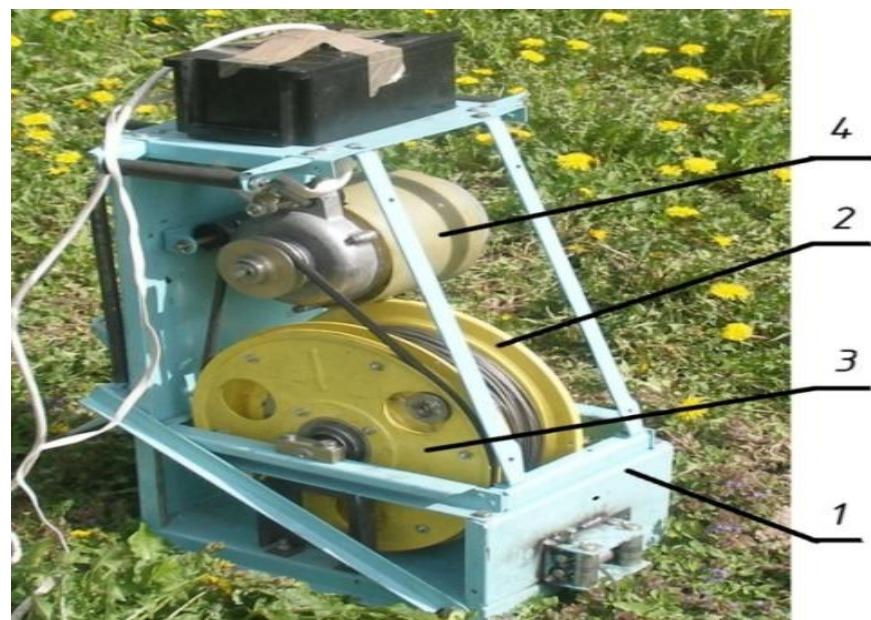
Общий вид экспериментального образца лебедки сельскохозяйственной, разработанной на основе прецессионного редуцирующего механизма: 1 – корпус лебедки; 2 – барабан с прецессионным редуктором; 3 – шкив; 4 – электродвигатель
